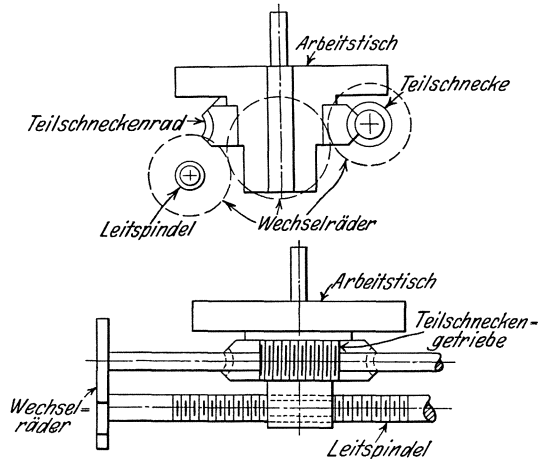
Schema des Wälzmechanismus einer Räderhobelmaschine mit zahnstangenartigem Werkzeug.
